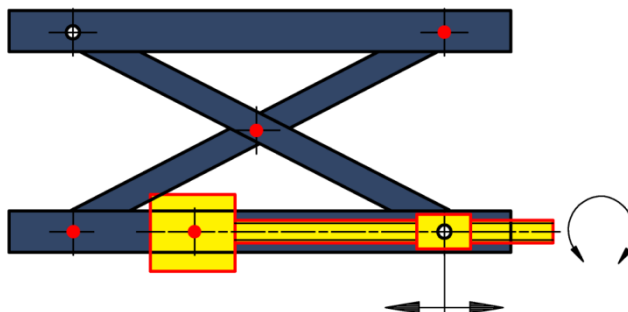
Umístění hydraulického válce u nůžkových plošin – varianta 3.
